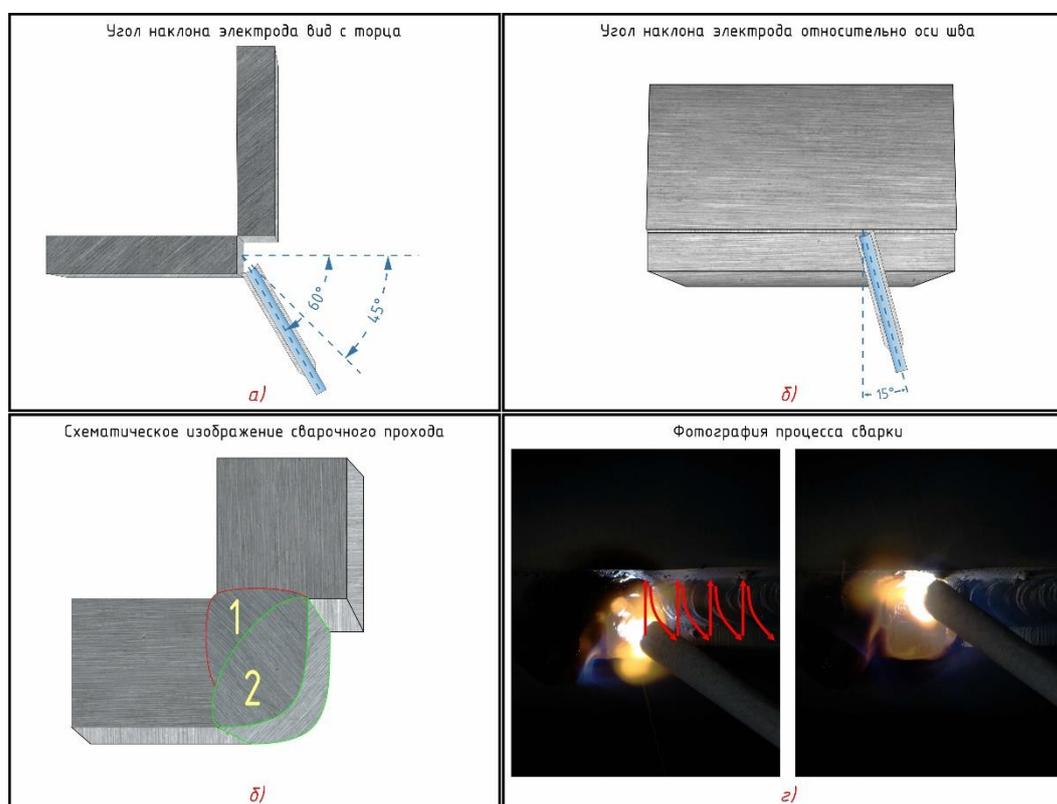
Положение электрода при сварке первого облицовочного прохода
